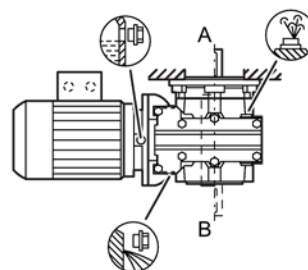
Монтажные положения для цилиндрического косозубого редуктора CF в исполнении с фланцем и CAZ с фланцем корпуса, типоразмер 29
